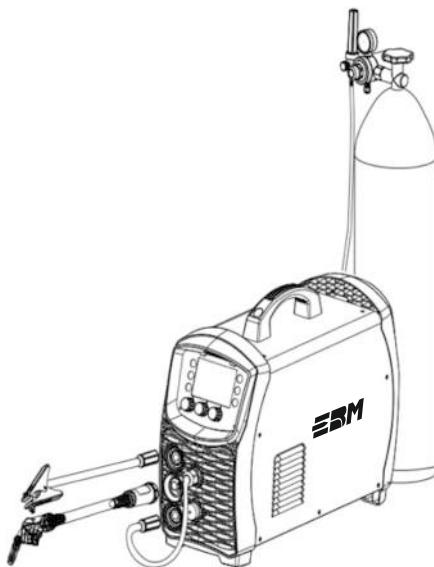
Схема подключения кабелей для MIG сварки
